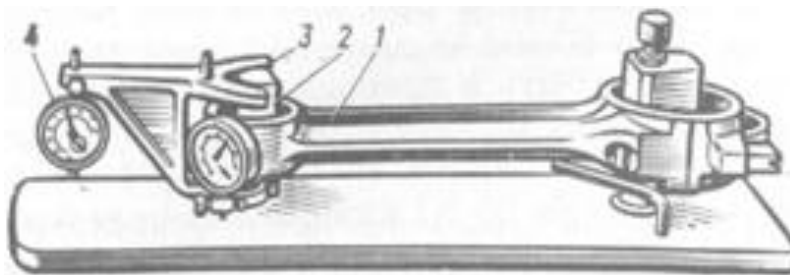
Схема измерения глубины фрезерования шатуна
